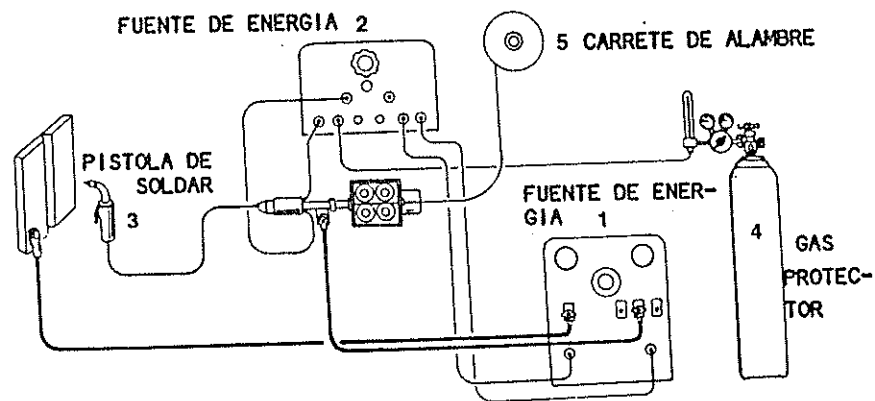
Equipo de soldadura MIG/MAG
